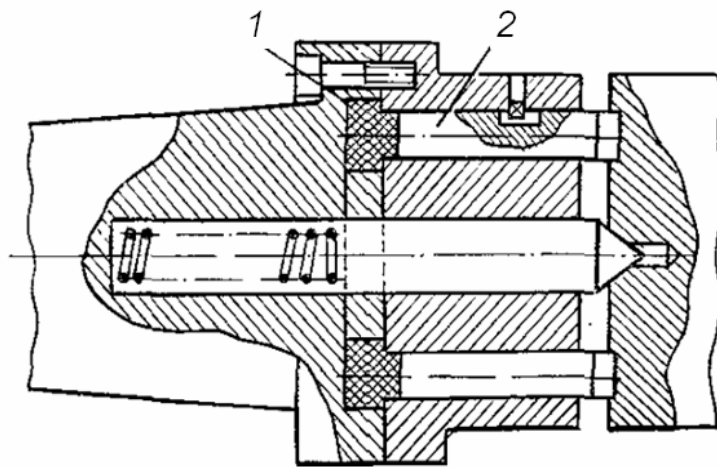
Повідцевий патрон з плаваючими штирками
